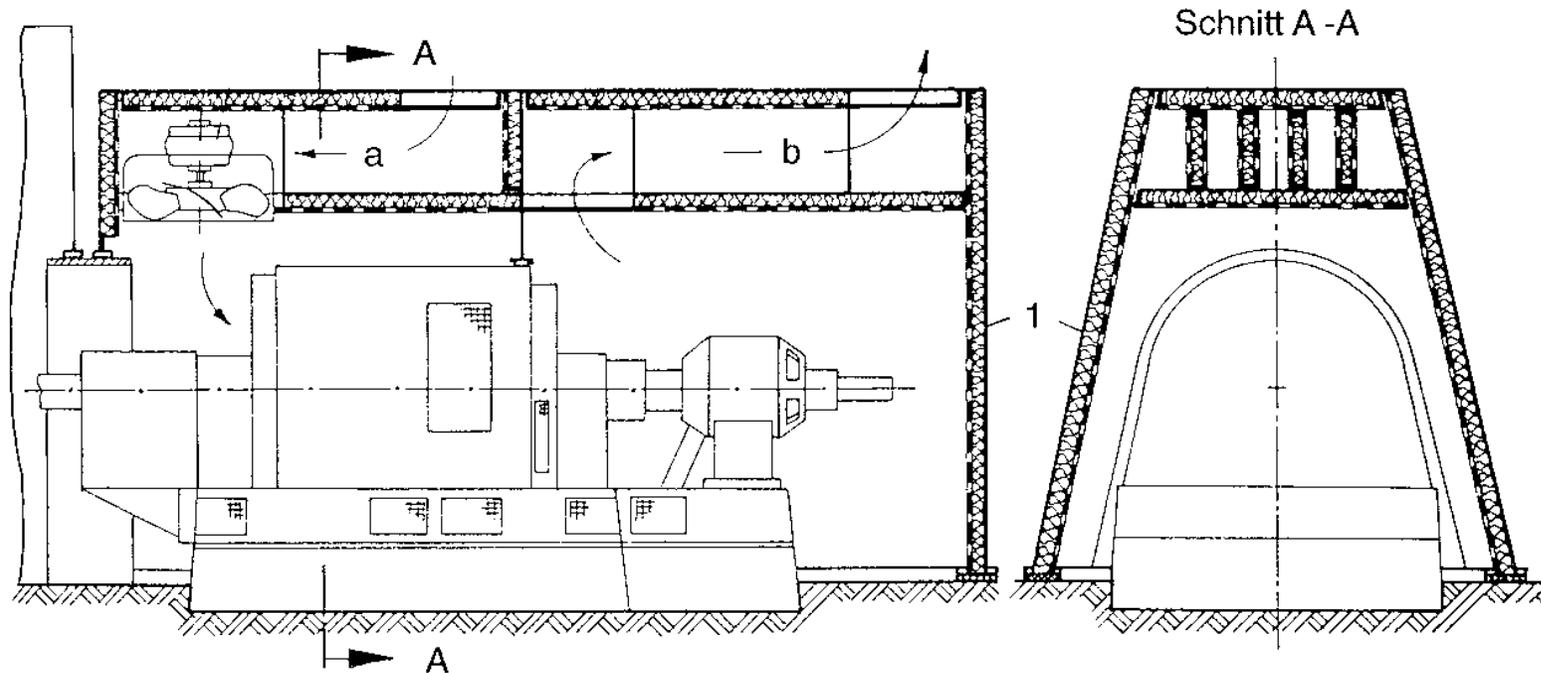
Kapsel für luftgekühlten Elektromotor mit Turbokompressor [1]
